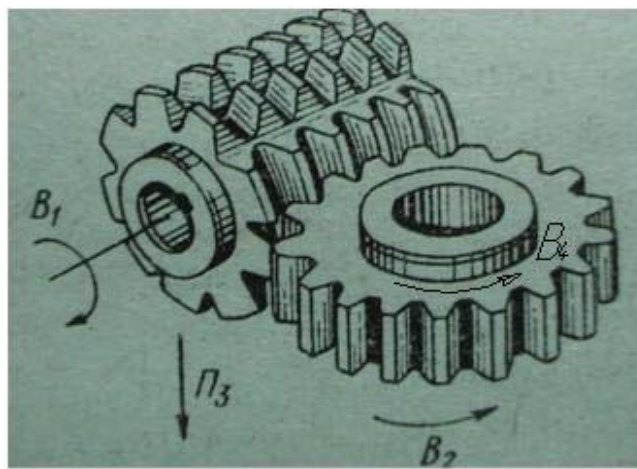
Формообразование зубьев цилиндрического колеса червячной фрезой
